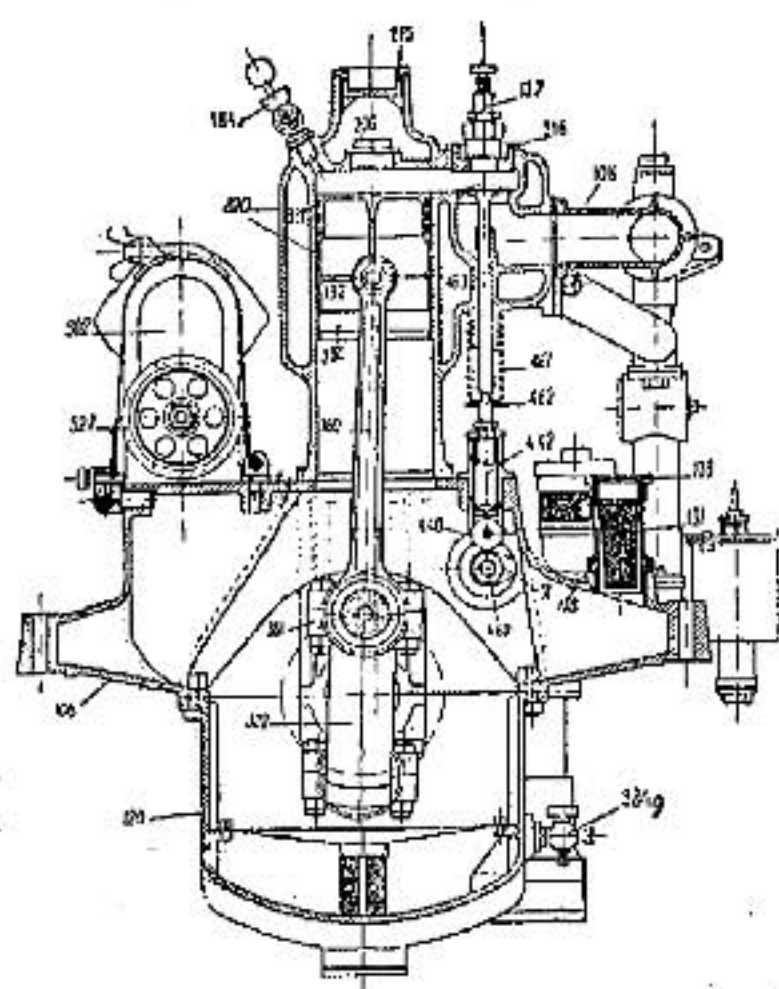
Поперечный разрѣзъ двигателя Протось.
